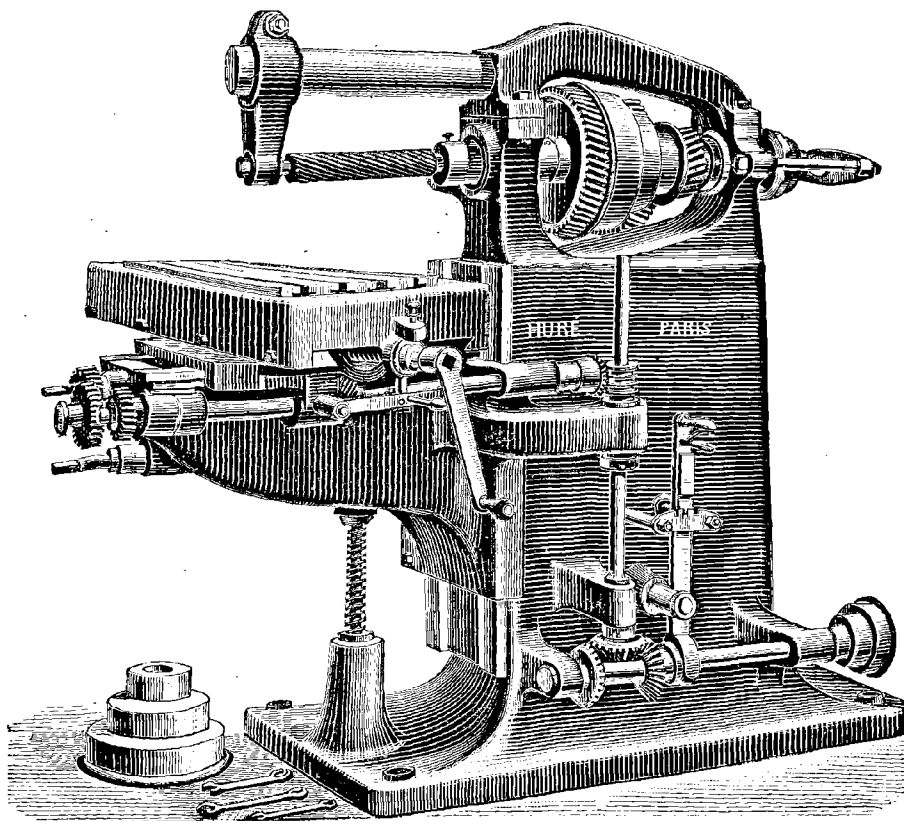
Machine à fraiser horizontale de M. Huré.
